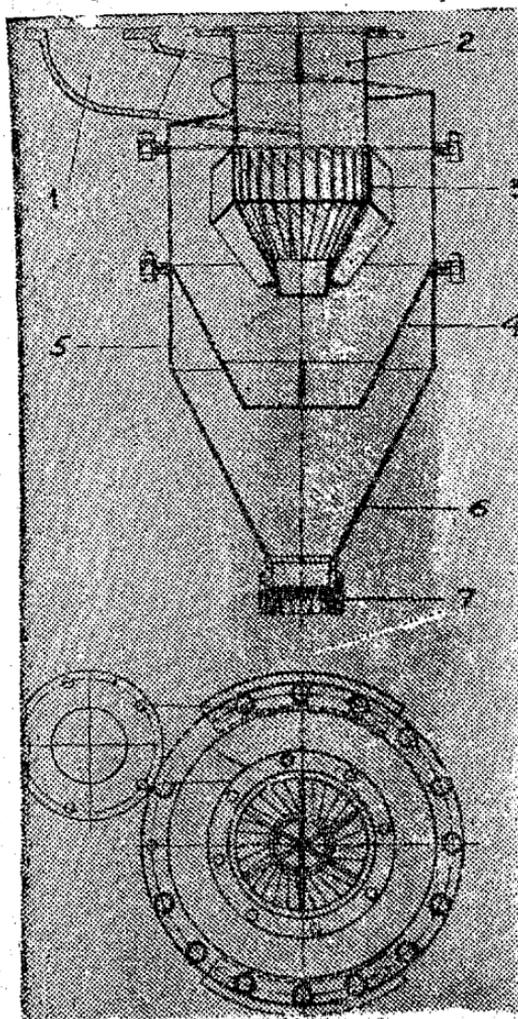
Циклонный очиститель в сборе: 1—патрубок подвода газа; 2—патрубок вывода газа; 3—лопатки; 4—конус верхнего корпуса; 5—цилиндр нижнего корпуса; 6—конус нижнего корпуса; 7—пробка.
